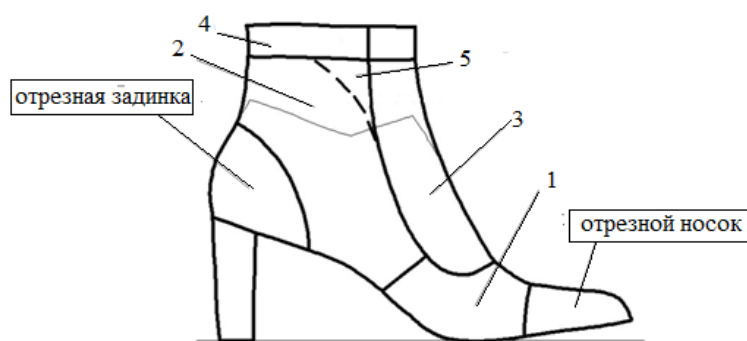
Схема расположения деталей из меха в конструкции ботинок: 1 – союзка, 2 – берец, 3 – передняя часть союзки (язычок), 4 – кокетка.
